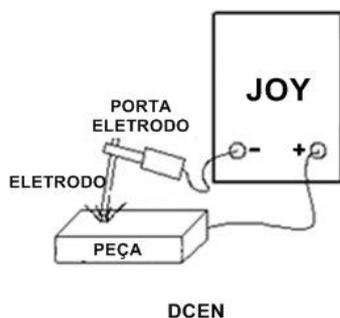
Conexão negativa para soldagem com eletrodo revestido
